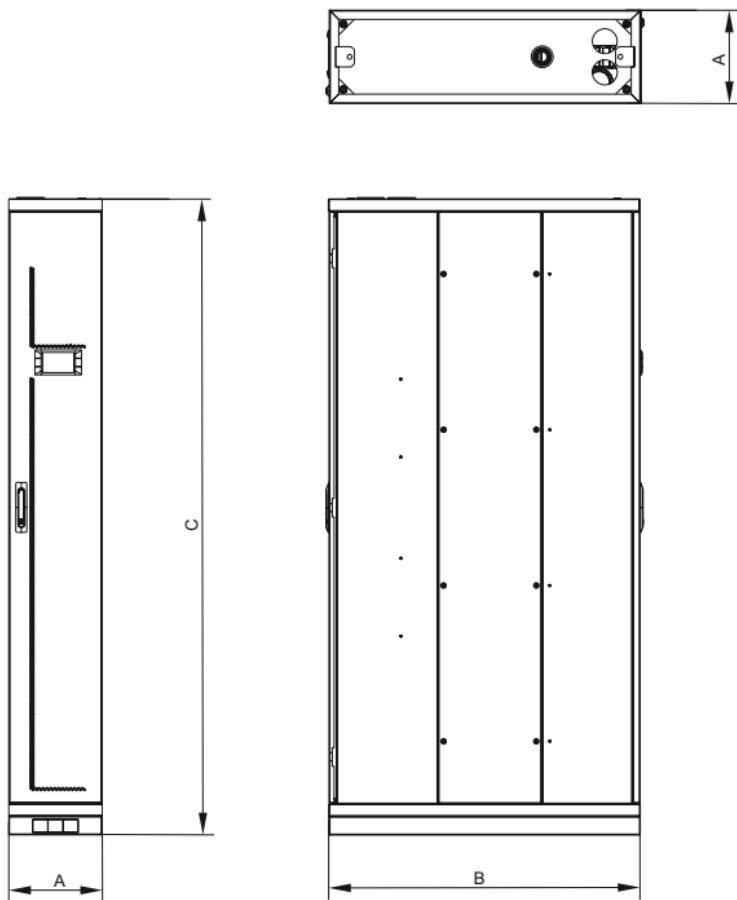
Габаритные размеры КПШ типа AIR CAB, FLUID CAB, WATER CAB /
